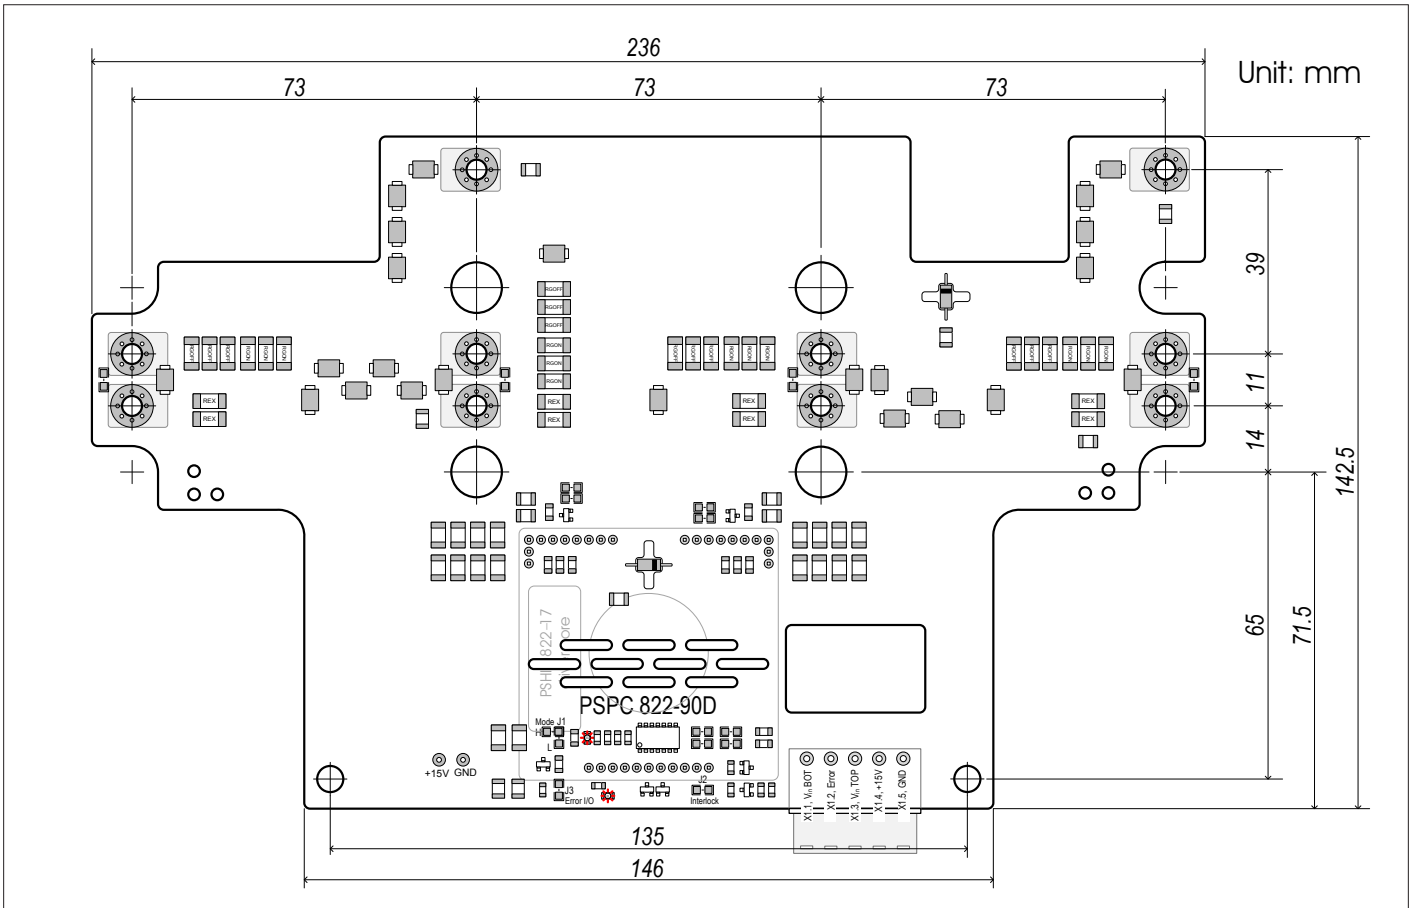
, PSPC 822-90D 双 IGBT 模块并联驱动器外形及安装尺寸示意图
